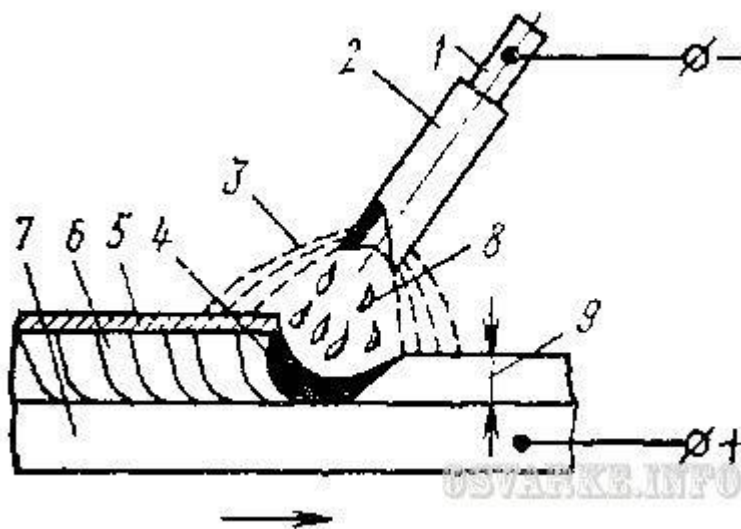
Схема ручной дуговой сварки металлическим электродом с покрытием (стрелкой показано направление сварки): 1 - металлический стержень, 2 - покрытие электрода, 3 - газовая атмосфера дуги, 4 - сварочная ванна, 5 - затвердевший шлак, 6 - закристаллизовавшийся металл шва, 7 - основной металл (изделие), 8 - капли расплавленного электродного металла, 9 - глубина проплавления
